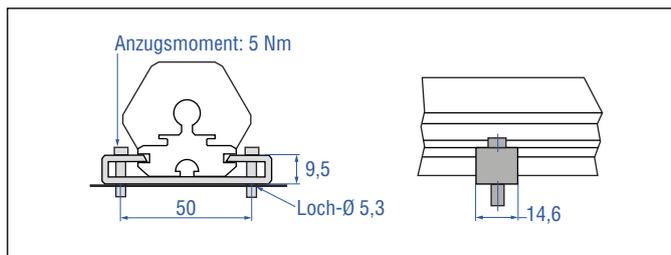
Montageklammern (Artikelnr. 400 802) mit Zylinderschraube M5×20
